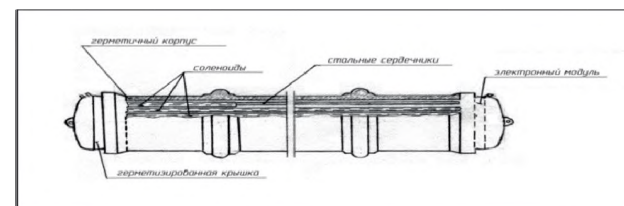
Общий вид магнитного модуля VMM трала – имитатора Sea Serpent
